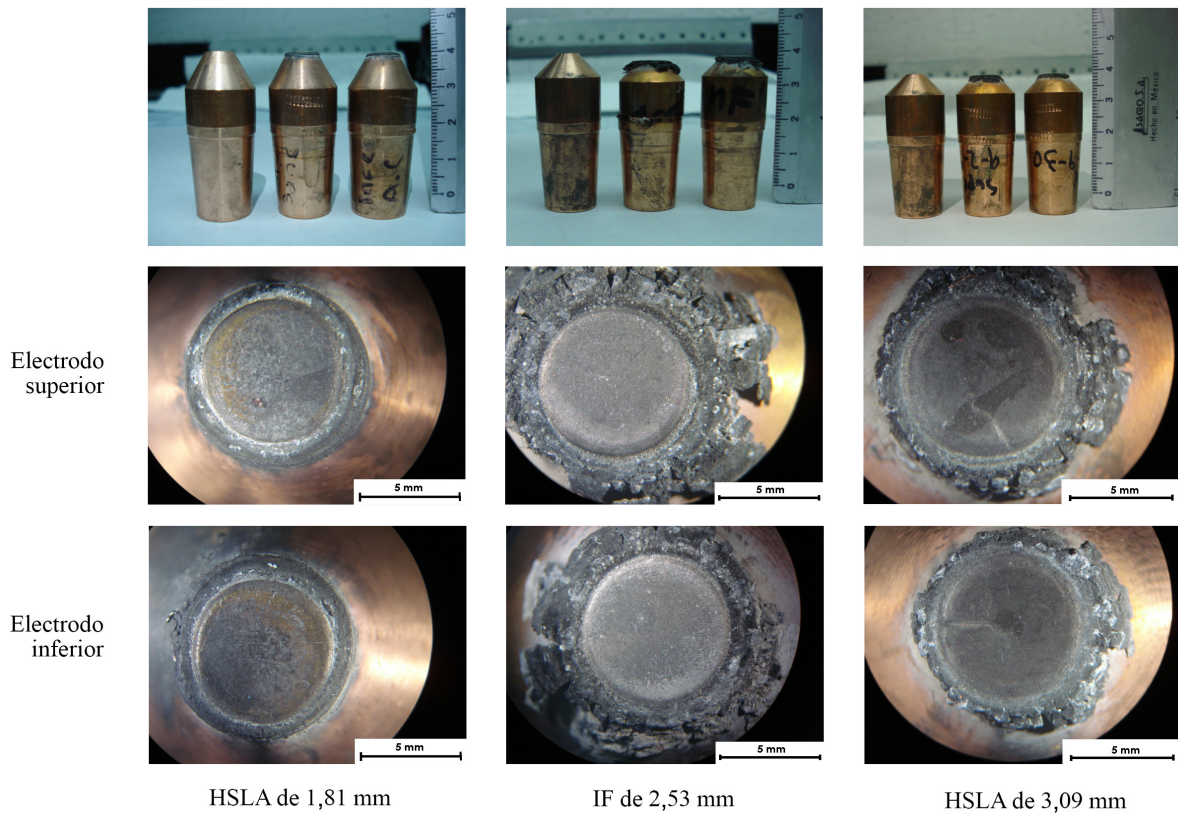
Desgaste de la cara de contacto de los electrodos después de 1.000 puntos de soldadura.
